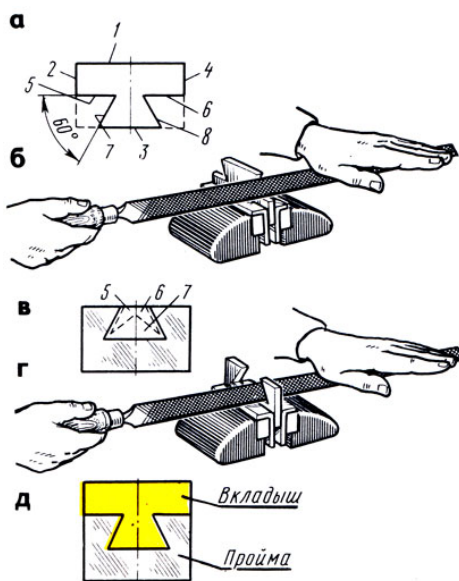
Припасовка косоугольных вкладышей: а - схема разметки наружных углов, б - опиление наружной поверхности, в - схема разметки внутренних углов, г - опиление внутренних углов, д - проверка вкладышем
